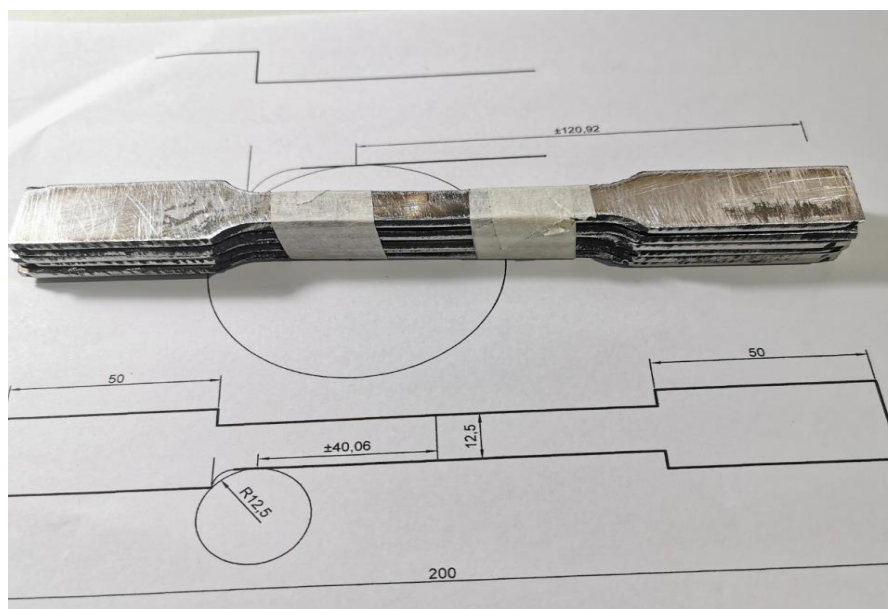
Probeta del Metal Base sin soldadura
